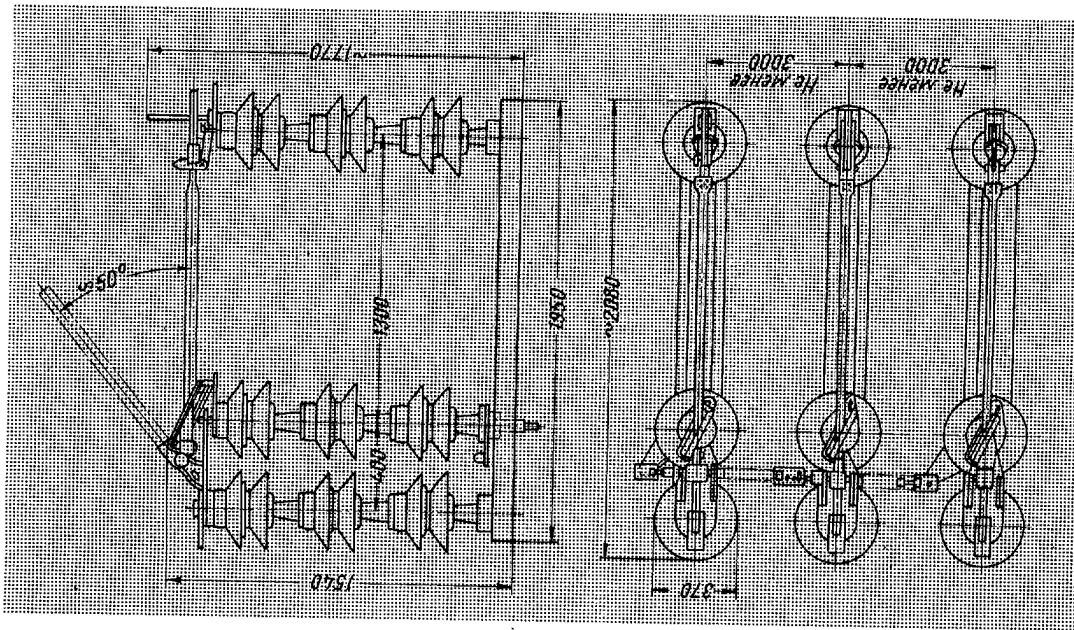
Габаритный эскиз разьединителя РЛН-110.
